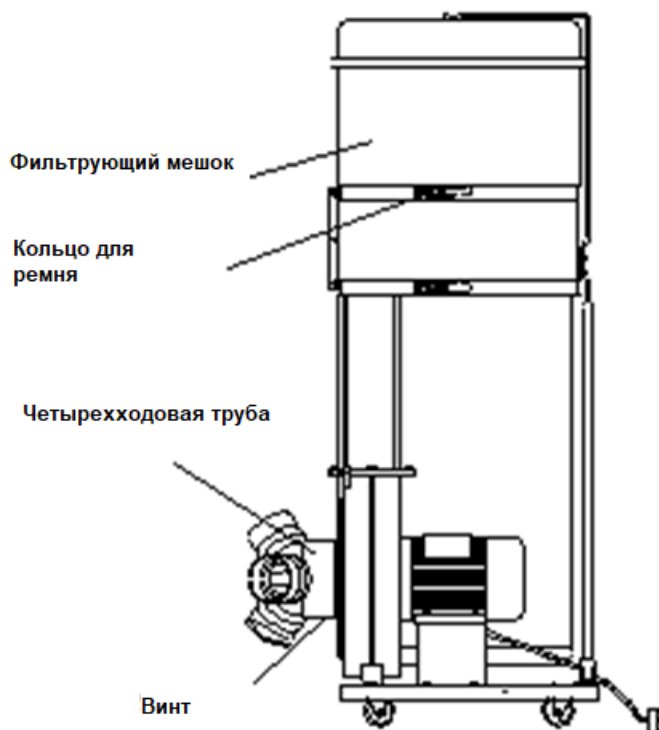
Установка фильтров, мешков-накопителей и коллектора
